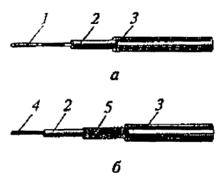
Монтажный провод с полихлорвиниловой изоляцией
